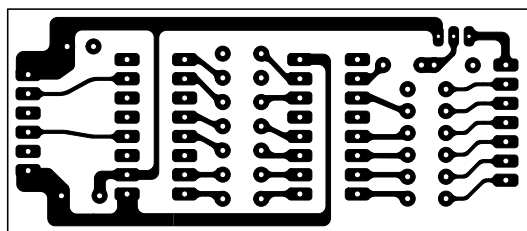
1: Dessin, à l'échelle 1, du circuit imprimé double face à trous métallisés de la platine des circuits intégrés EN1676B, côté soudures.
